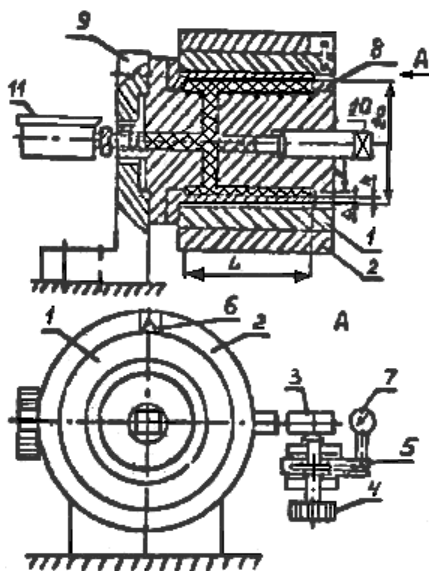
Схема экспериментальной установки для определения усилия зажима заготовки на оправке с гидрпластмассой
